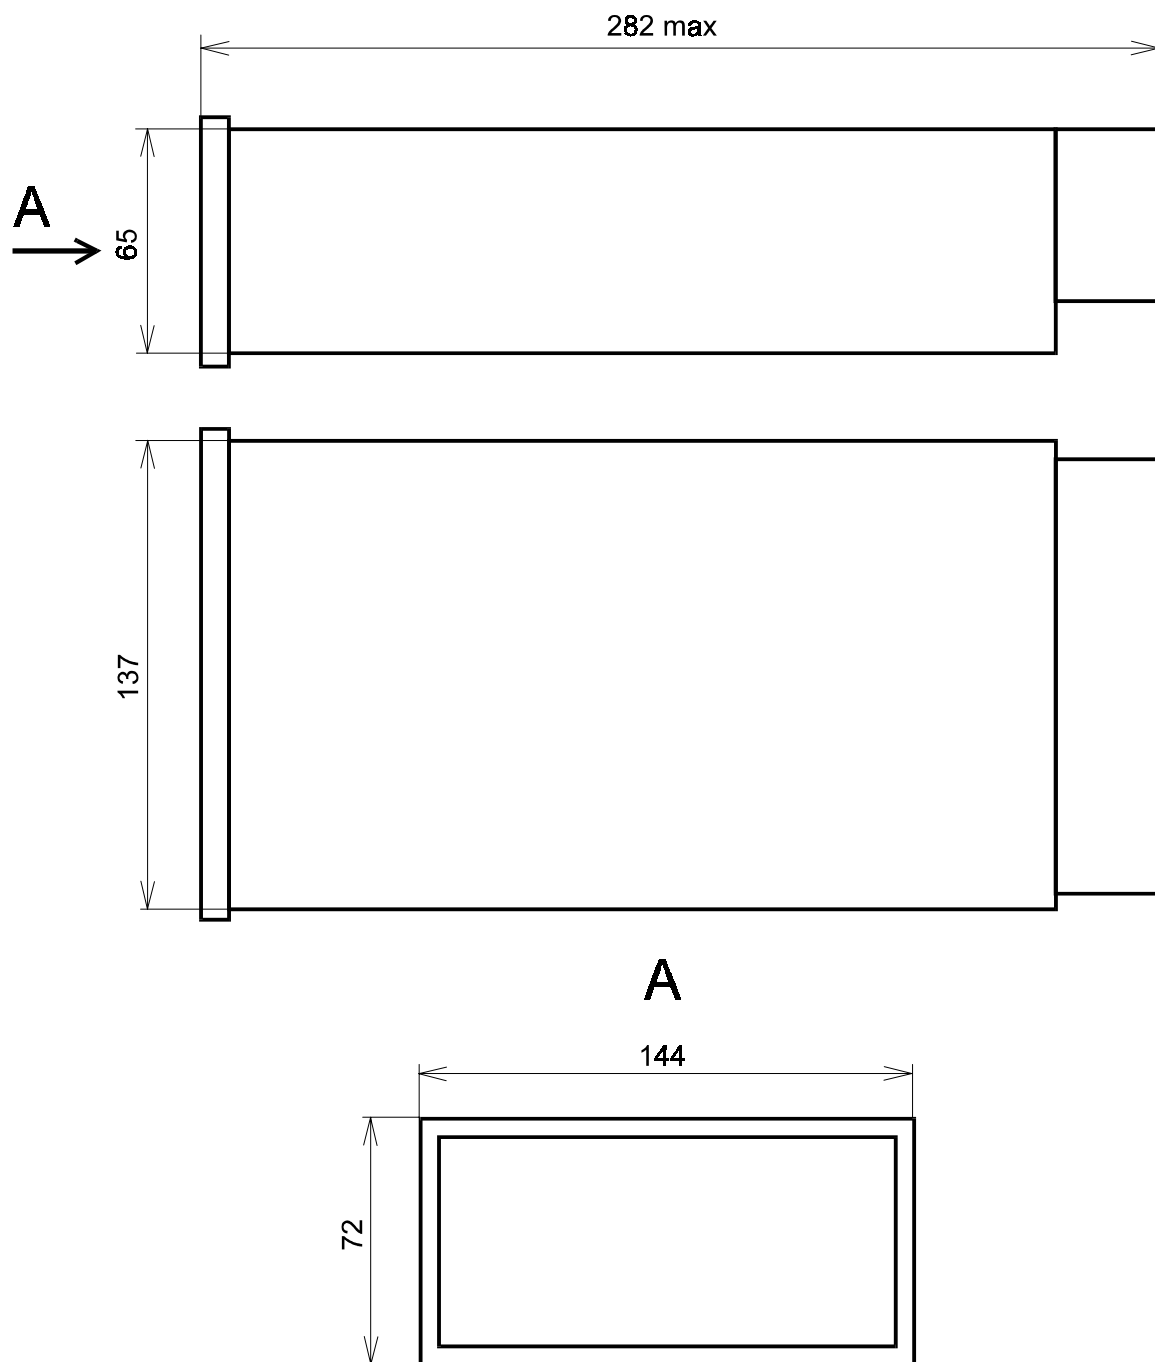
Габаритные и установочные размеры вычислительного блока щитового исполнения
